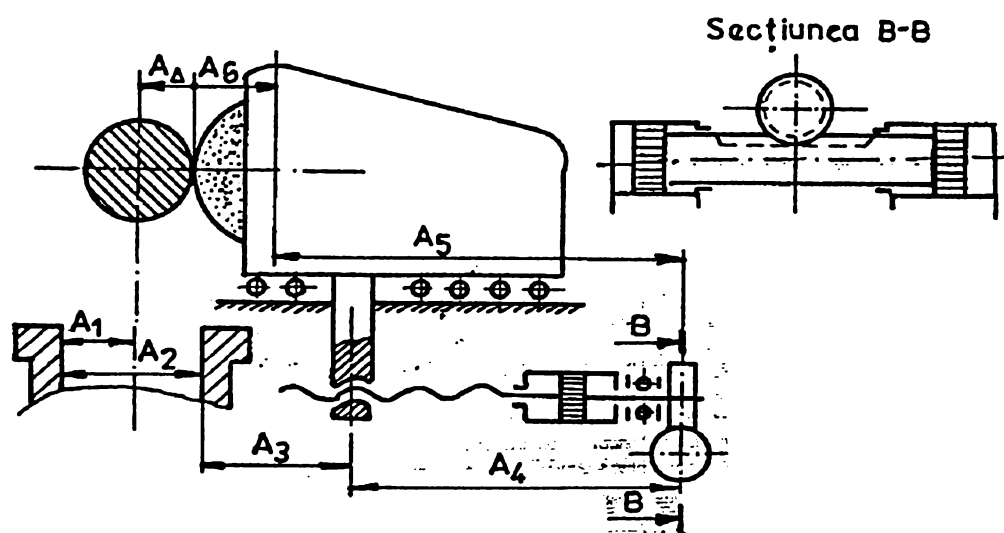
Lanțul de dimensiuni la rectificarea rotundă exterioară
